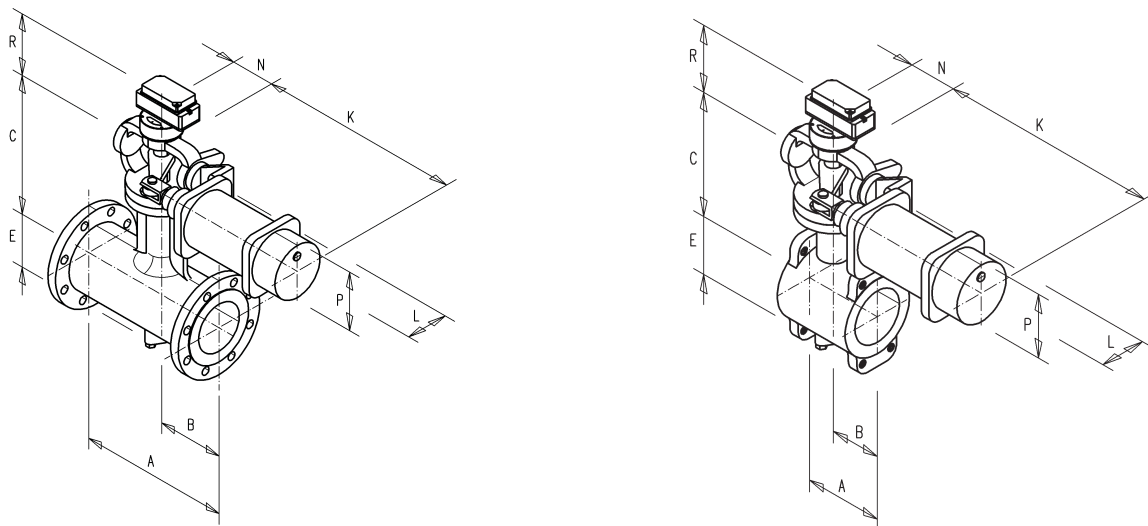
· Maßbild für VETEC-Drehkegelventil Typ 72.3 R in Flansch- und Typ 72.4 R in Sandwichbauweise
